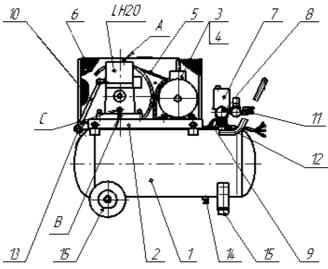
Общий вид компрессора CБ-4/C-50.*LH*20, CБ4/C-50.*LH*20A
